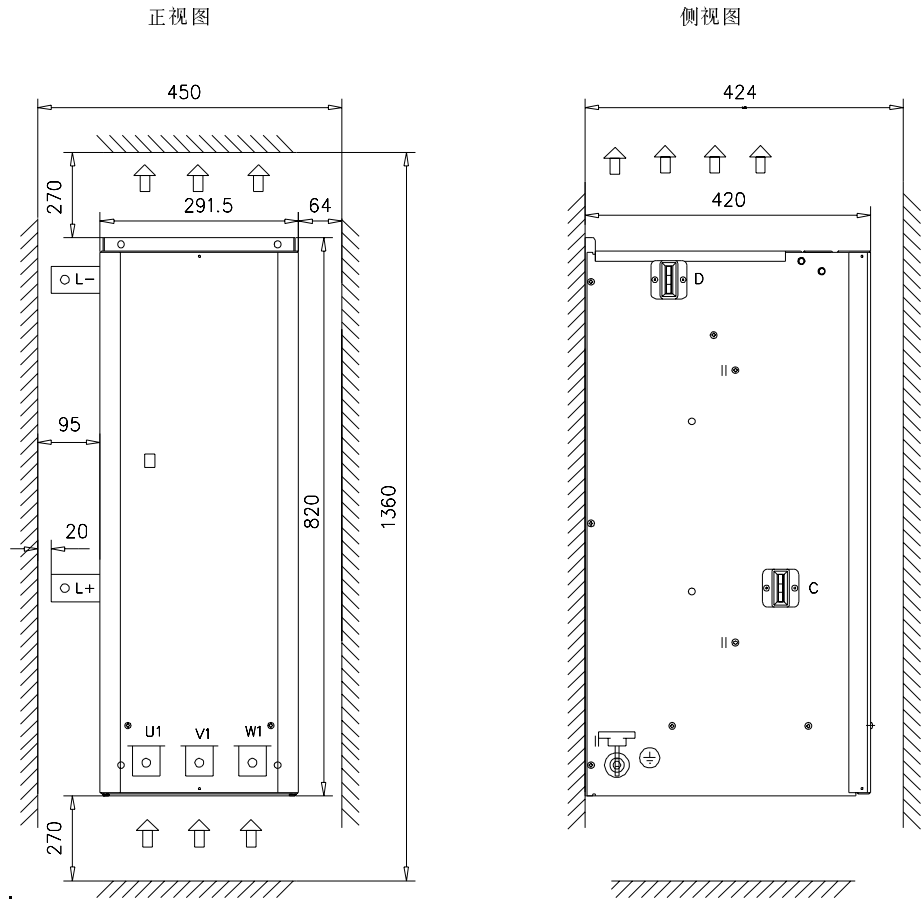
外形尺寸 B3 供电模块的尺寸和间距
